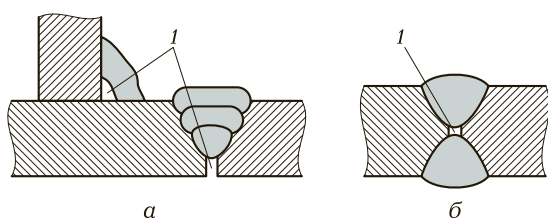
Непровары корня углового и стыкового односторонних (а) и стыкового двухстороннего (б) сварных швов:
